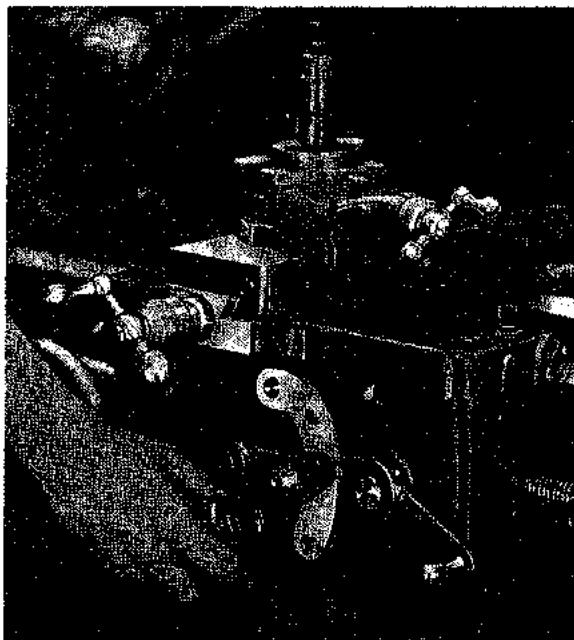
La fuerza de avance del carro es regulada mediante un pequeño volante dispuesto en el delantal (South Bend Lathe Works).
